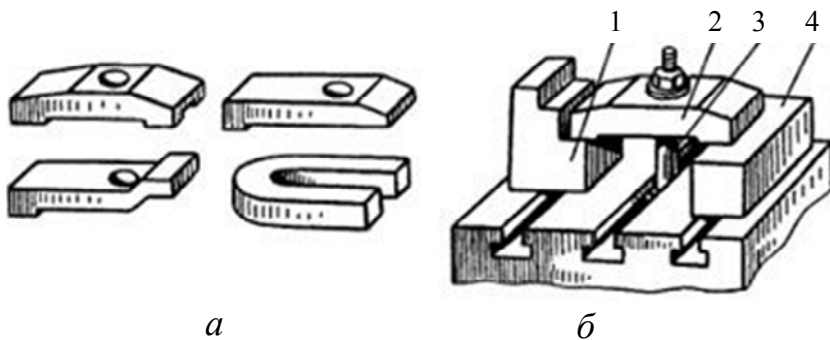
Прихваты и подставка: а – прихваты для крепления детали непосредственно на столе станка; б – прихват, опирающийся на подставку: 1 – подставка; 2 – прихват; 3 – болт; 4 – заготовка
